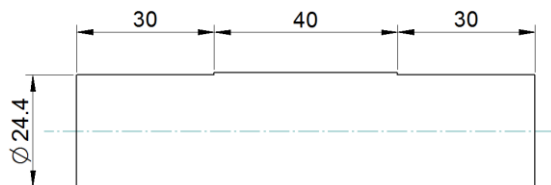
Desenho dos corpos de prova usinados- própria autora.
